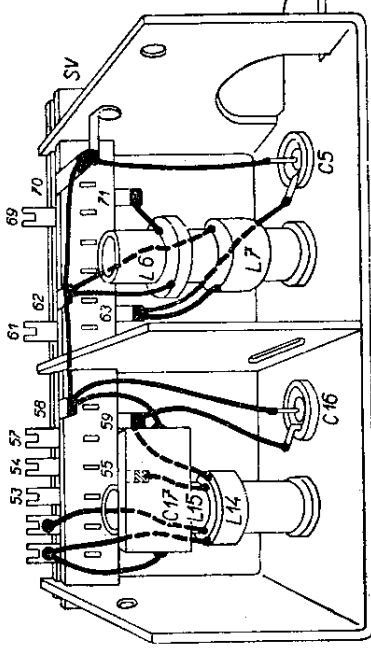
Zapojení tlačítka zespodu s vyznačenými přípojnými body
